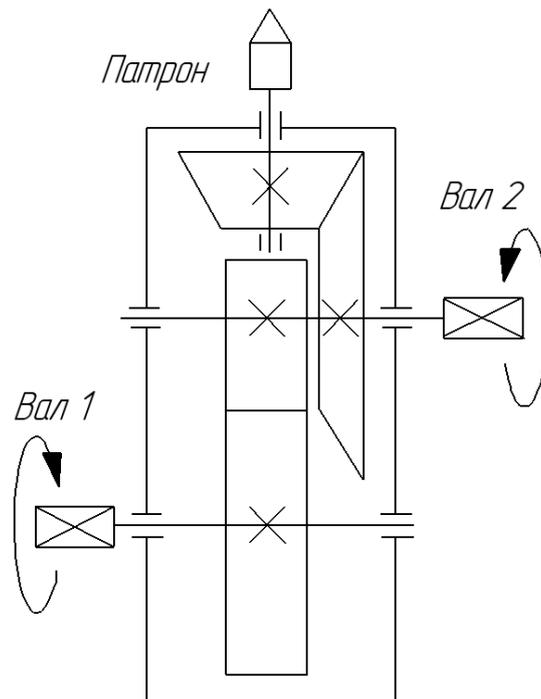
Кинематическая схема редуктора ручной дрели.
